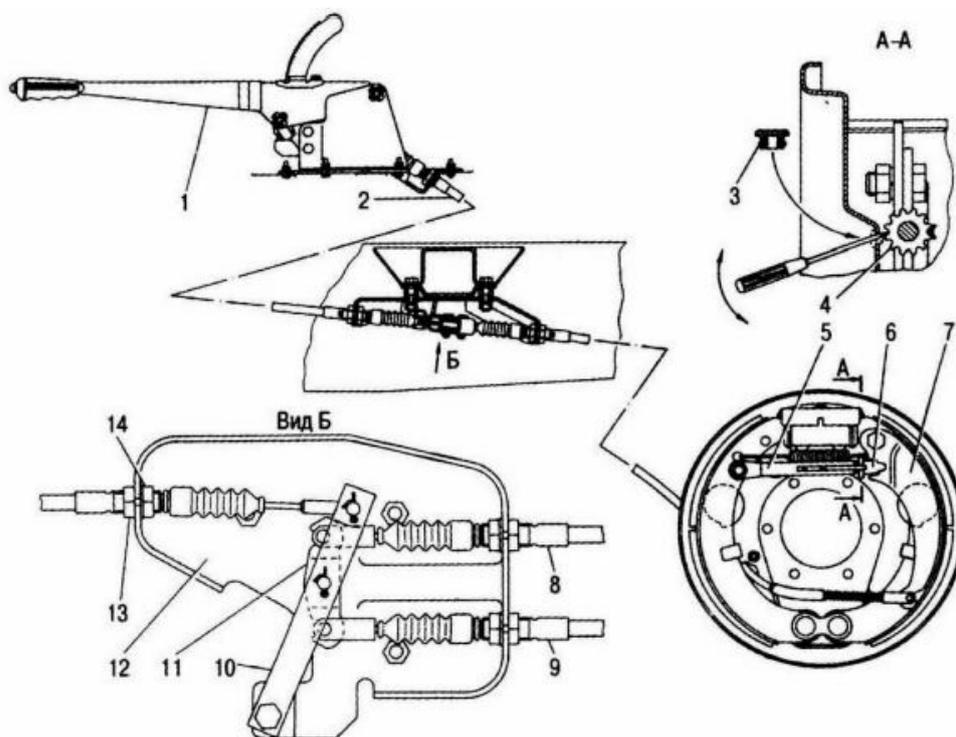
Стояночная тормозная система: 1 – рычаг; 2 – передний трос; 3 – заглушка; 4 – регулировочный винт; 5 – разжимное звено; 6 – опорная втулка; 7 – рычаг привода; 8, 9 – задние тросы; 10 – рычаг уравнивателя; 11 – уравниватель; 12 – кронштейн; 13 – регулировочная гайка; 14 – контргайка
